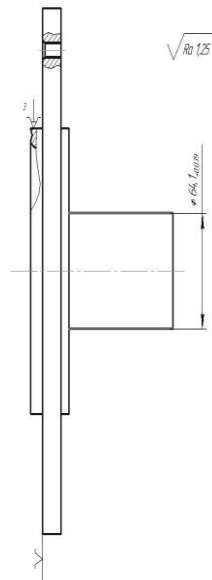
Фланець ведучої частини маточини колеса
